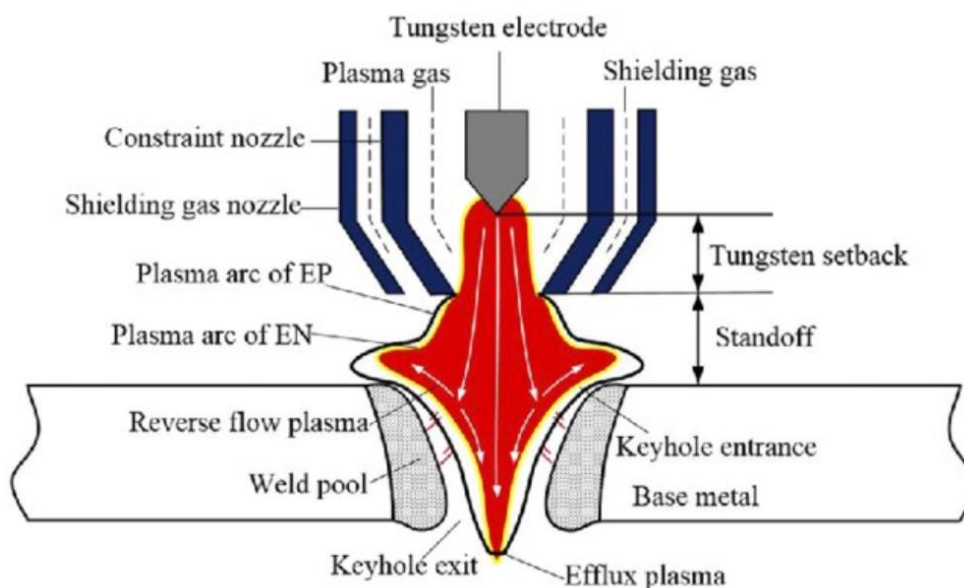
Схема плазово-дугового зварювання із різнополярним асиметричним струмом [8]
